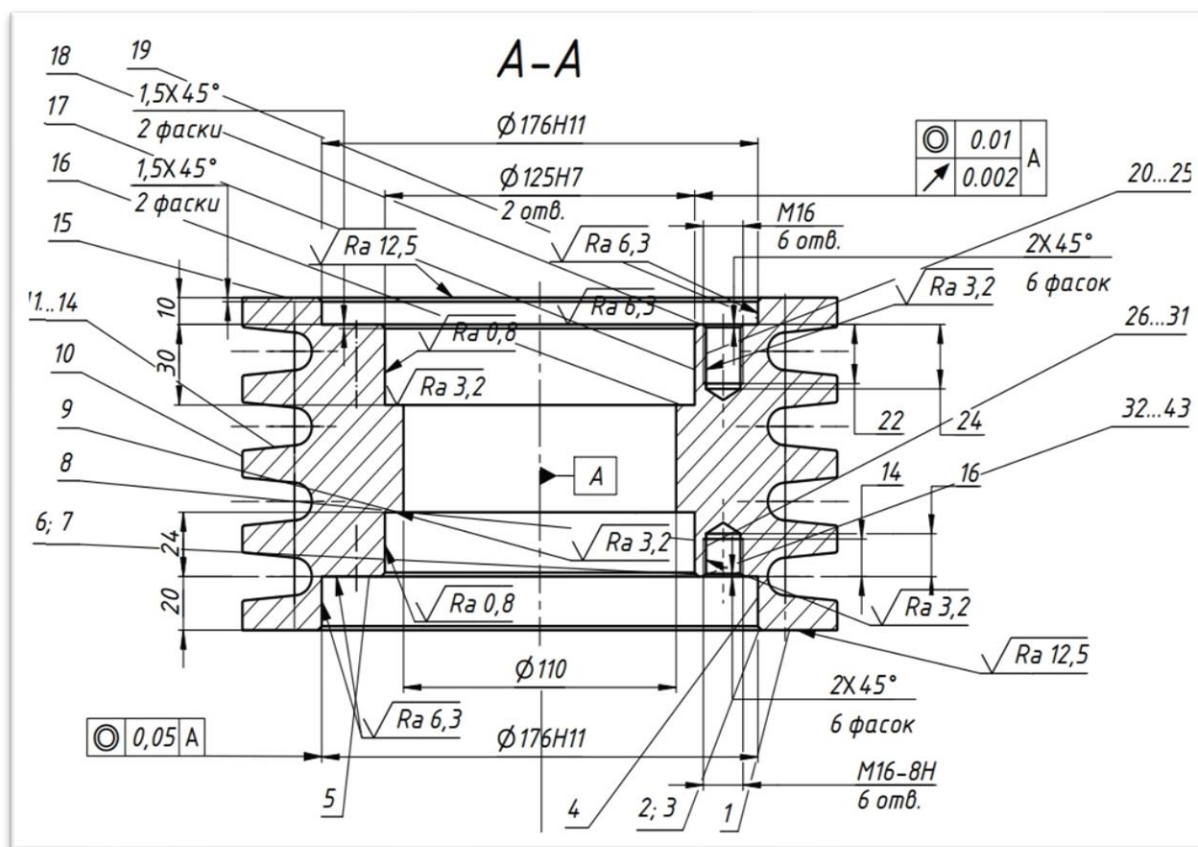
Основні оброблювані поверхні деталі «Ролик 2612.22»
